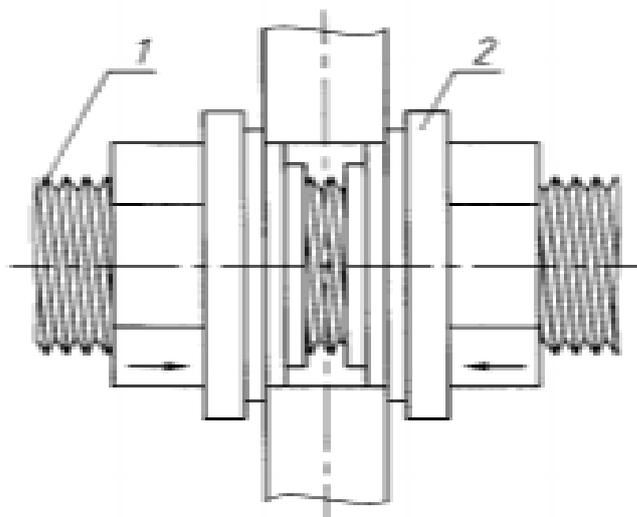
Конструкция гаек со ступенчатыми поверхностями
